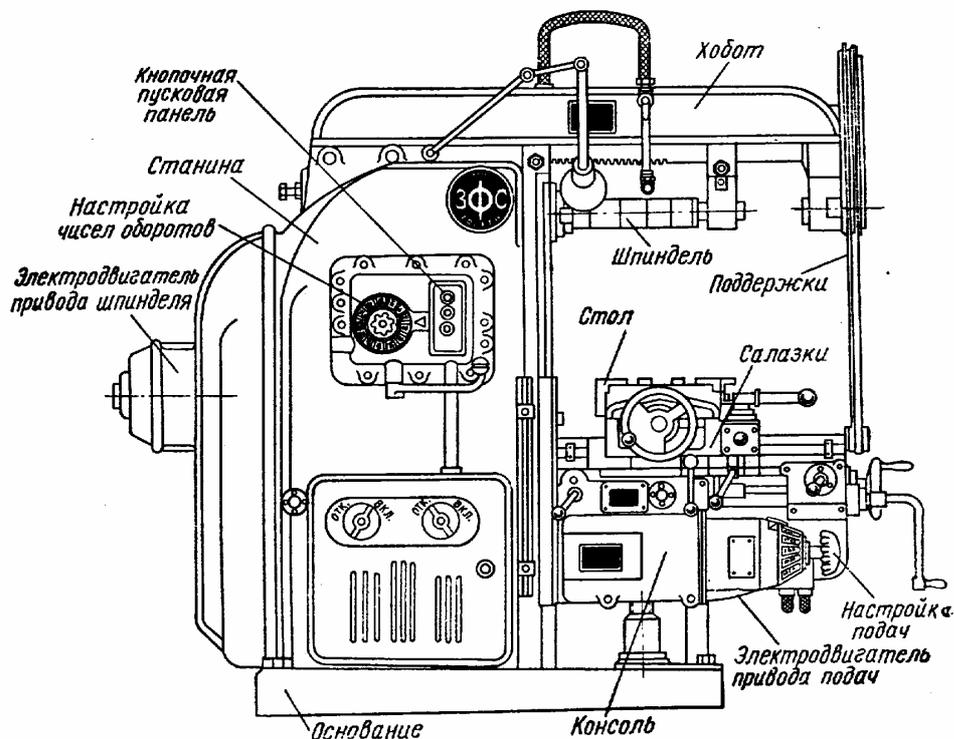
Горизонтально-фрезерный станок 6H82Г
